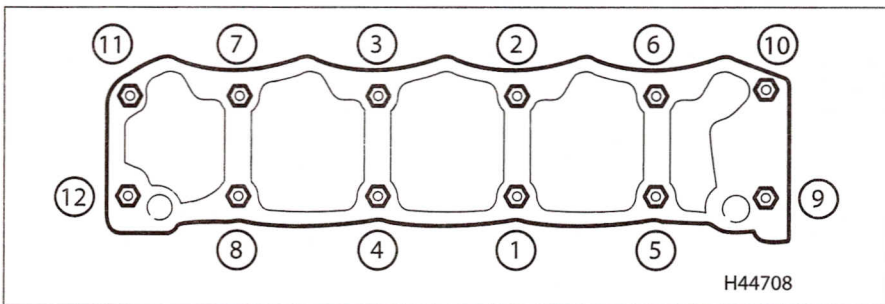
Последовательность затяжки болтов крепления корпуса подшипников распределительных валов (двигатели 1.6 л)
